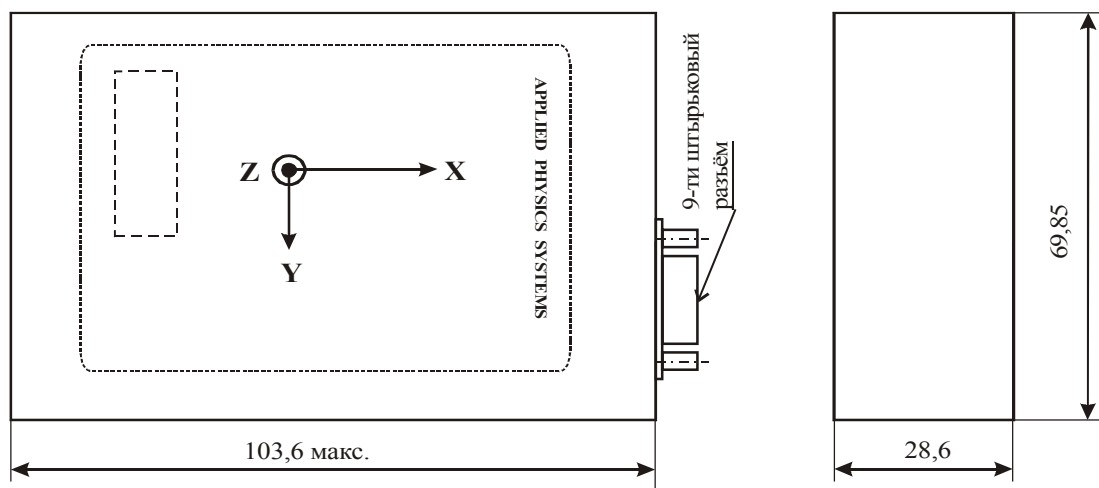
Внешний вид и габаритные размеры датчика типа APS-543
